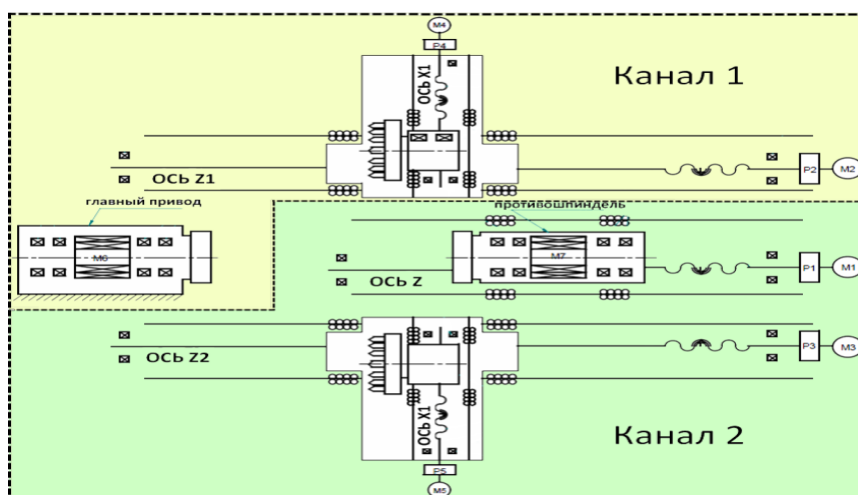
Кинематическая схема обрабатывающего центра наклонной компоновки.
